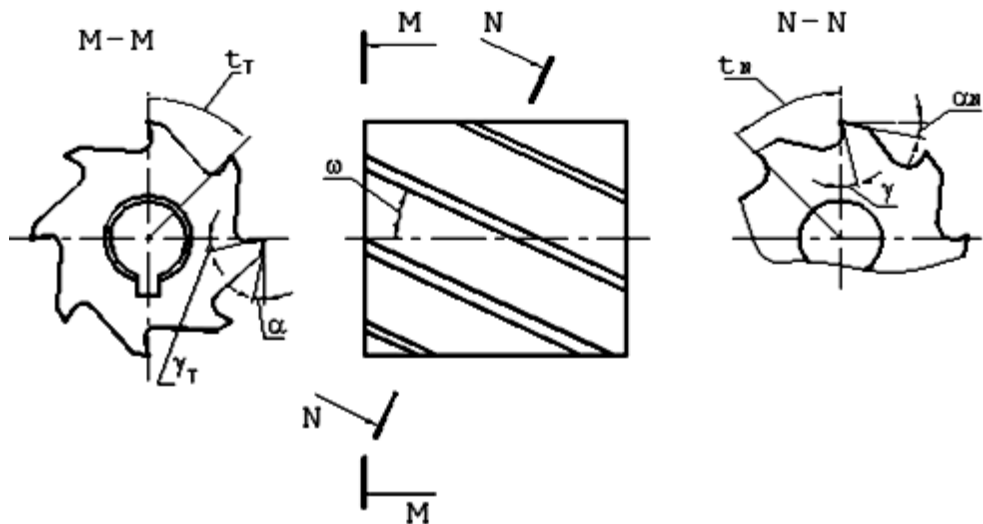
Геометрические параметры режущей части цилиндрической фрезы
